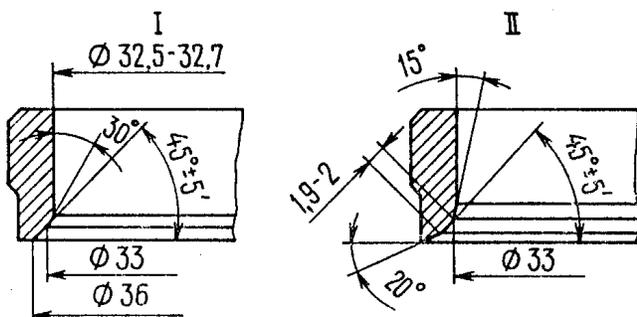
Perfil del asiento de la válvula de admisión:
